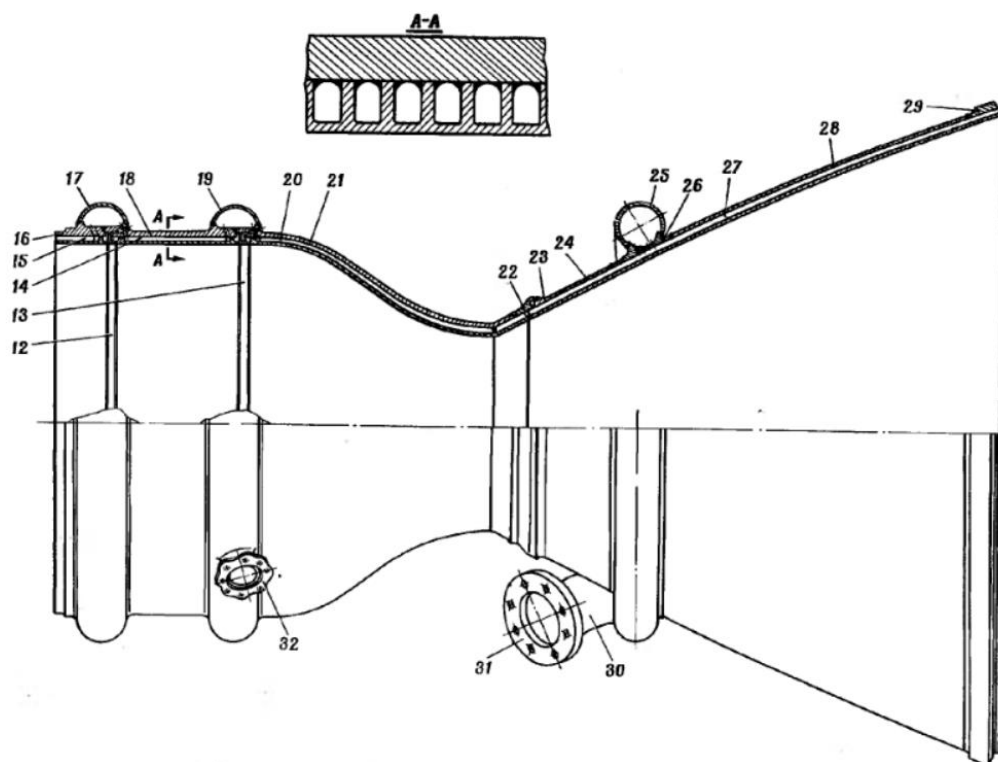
Ескіз корпусу камер РД-114 и РД-115
